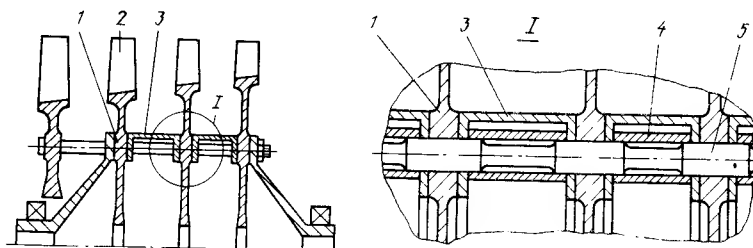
Ротор барабанно-дискового типа с длинными призонными болтами для стягивания дисков
